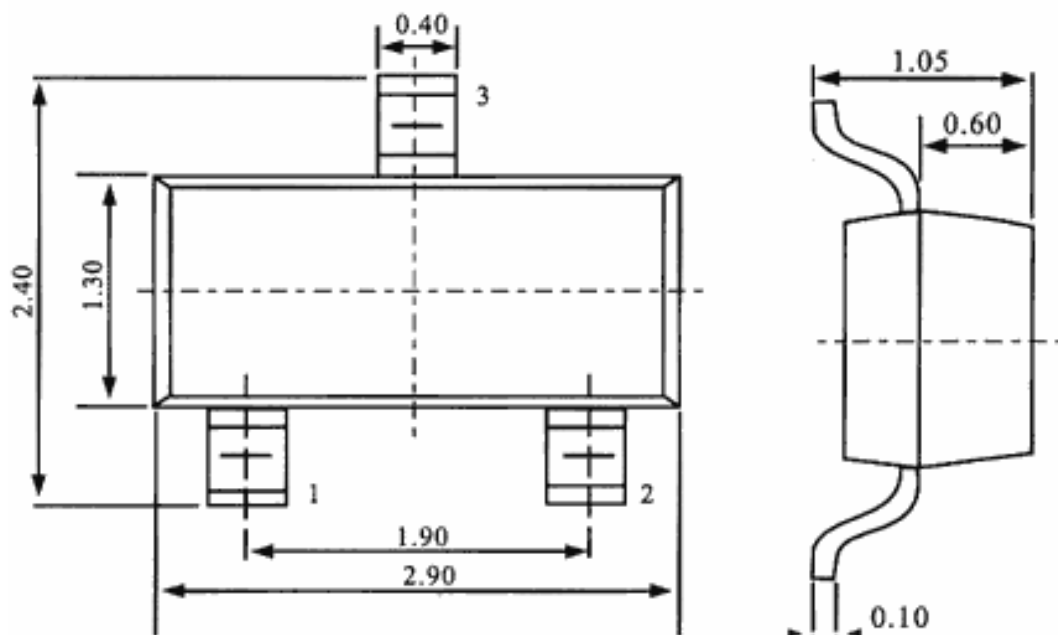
Габаритні розміри корпусу SOT-23
